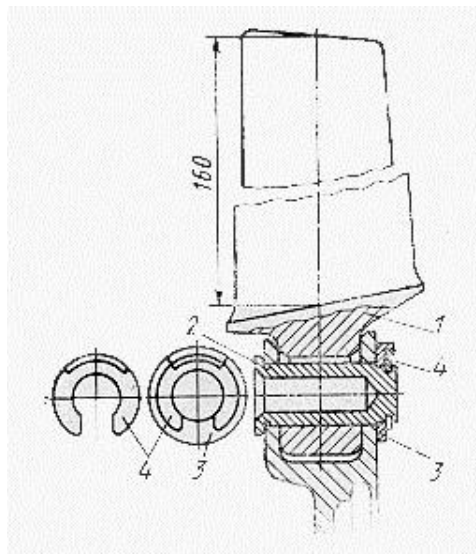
Шарнирное крепление лопаток компрессора:
